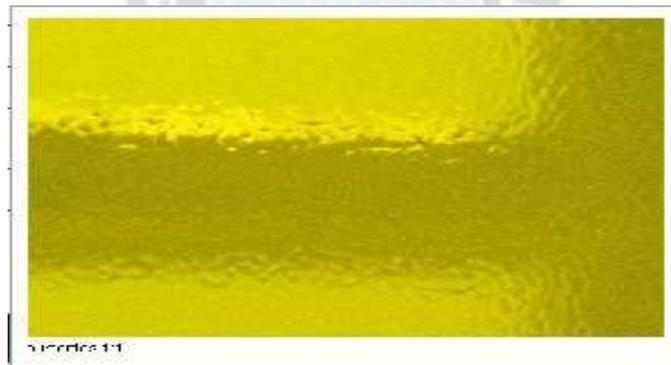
Efecto de piel de naranja (pintado pobre)
